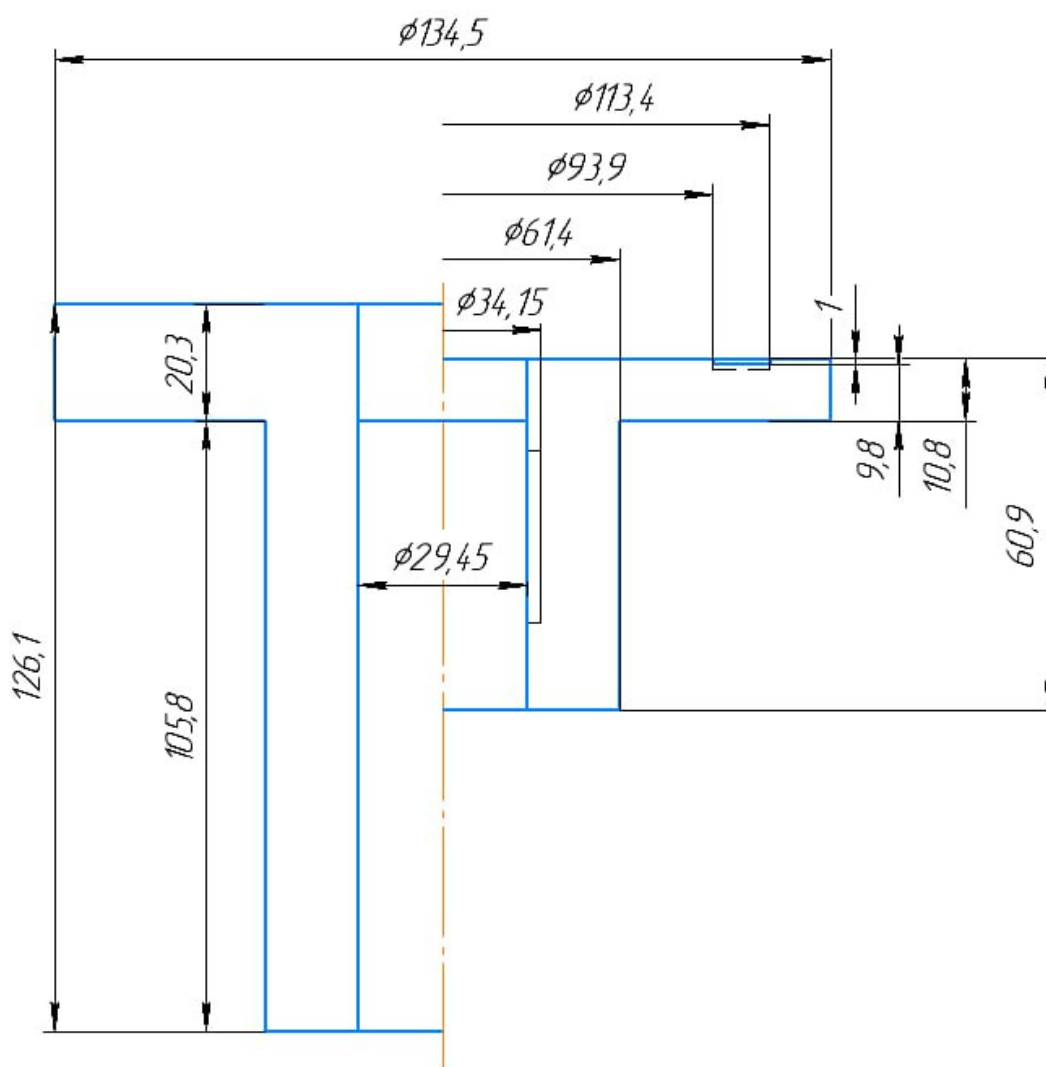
Размеры заготовки перед спеканием и размеры засыпки порошка в пресс-форме.
